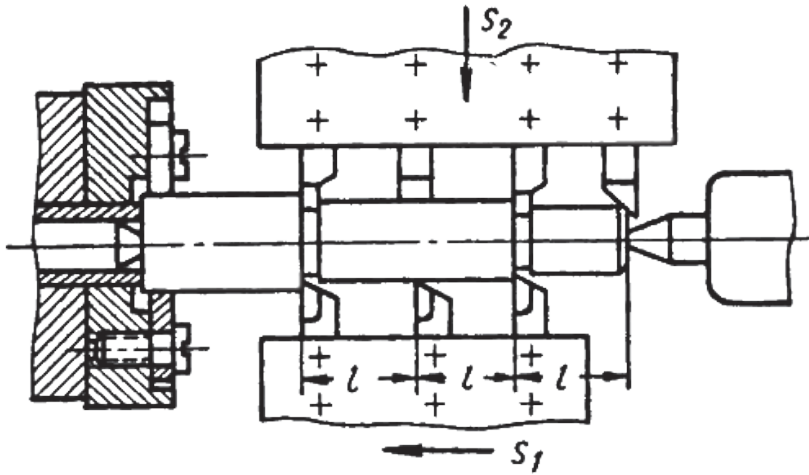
Обробка ступінчастого валика на багаторізцевому верстаті
